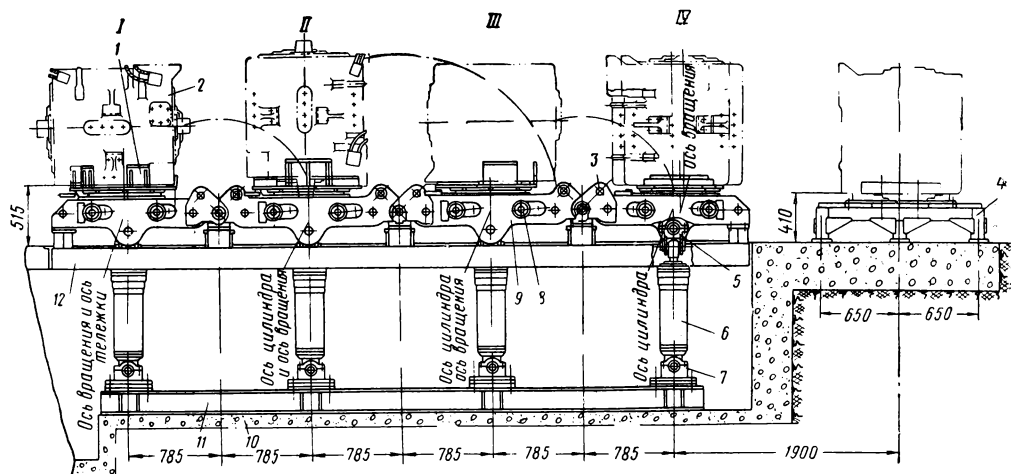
Конвейер для кантовки и перестановки тяговых двигателей при разборке:
